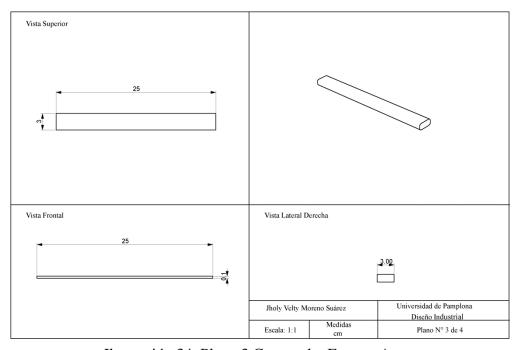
Plano 3 Cargatodo. Fuente: Autor
